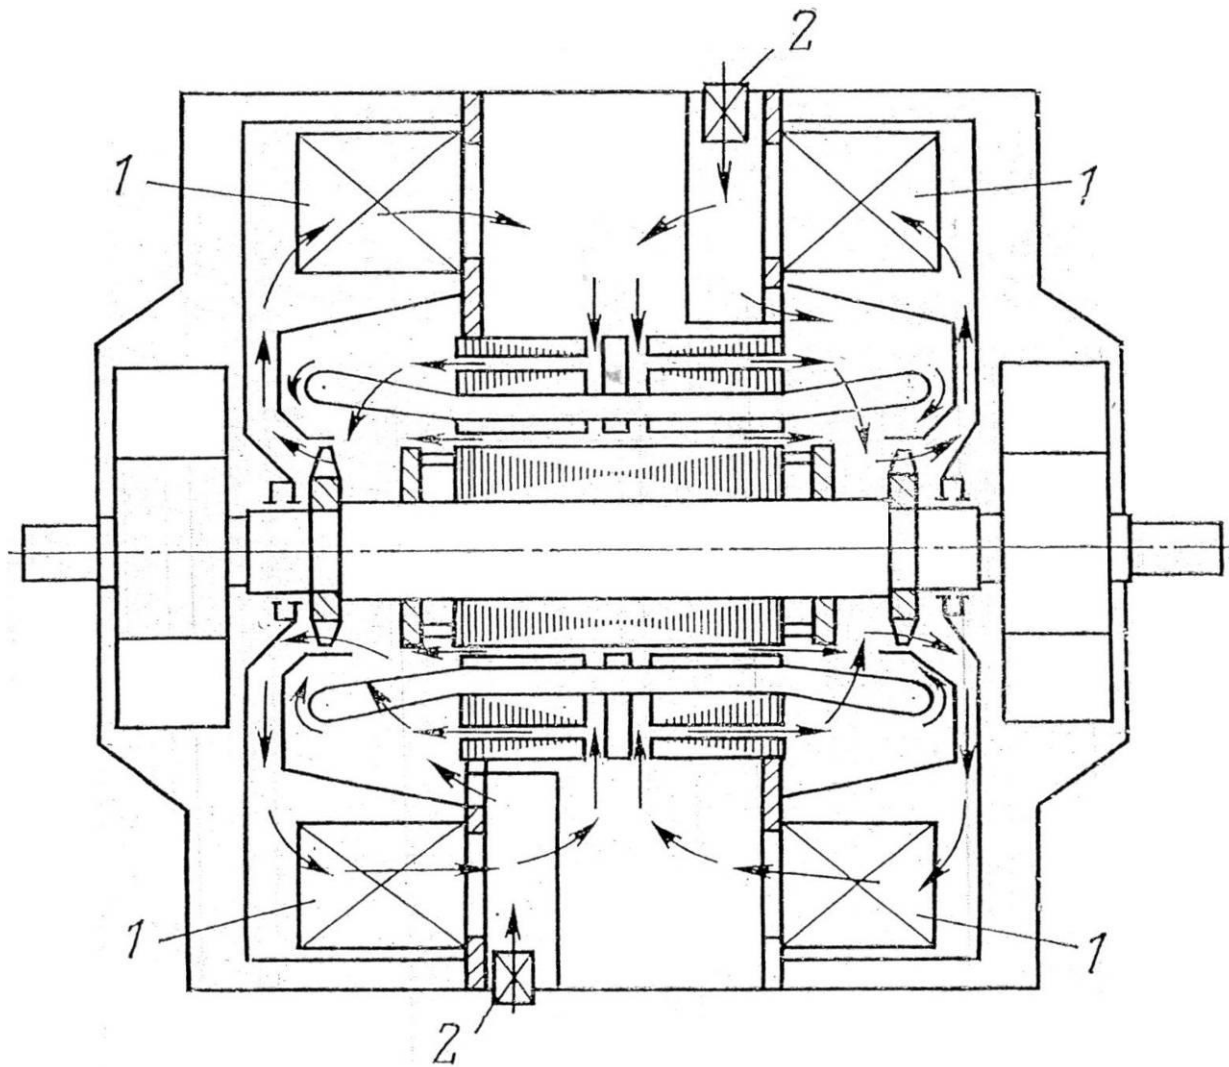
Схема вентиляции электродвигателей 2АЗМ-1600, 2АЗМ-2500 и 2АЗМ-5000 (с замкнутой схемой вентиляции).
